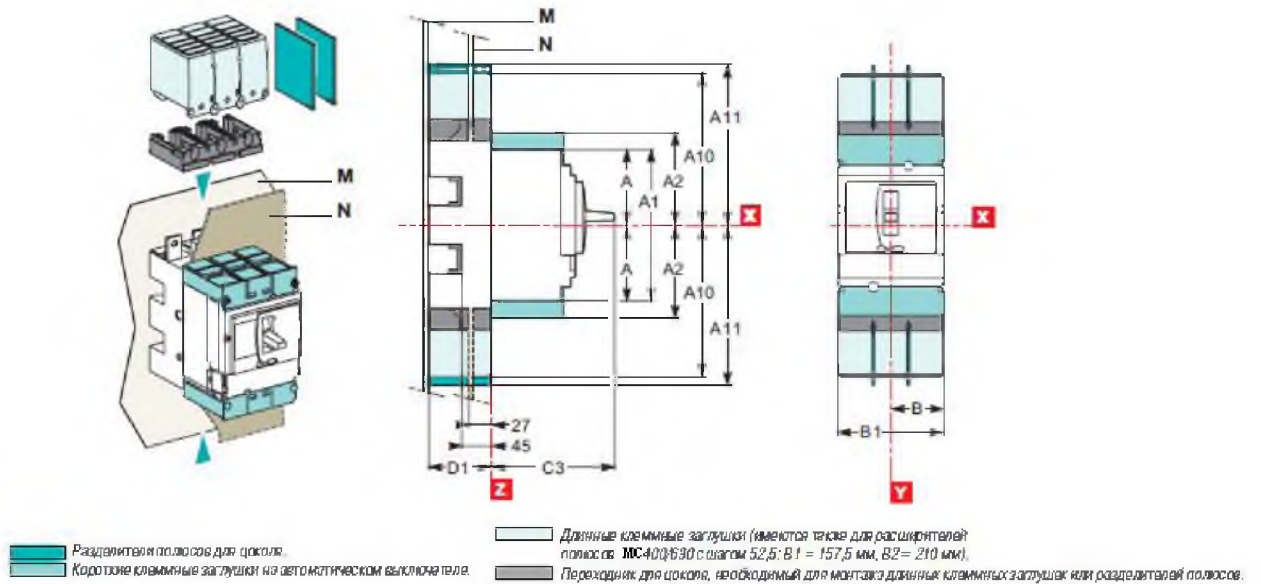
Габаритные размеры втычного исполнения выключателя
